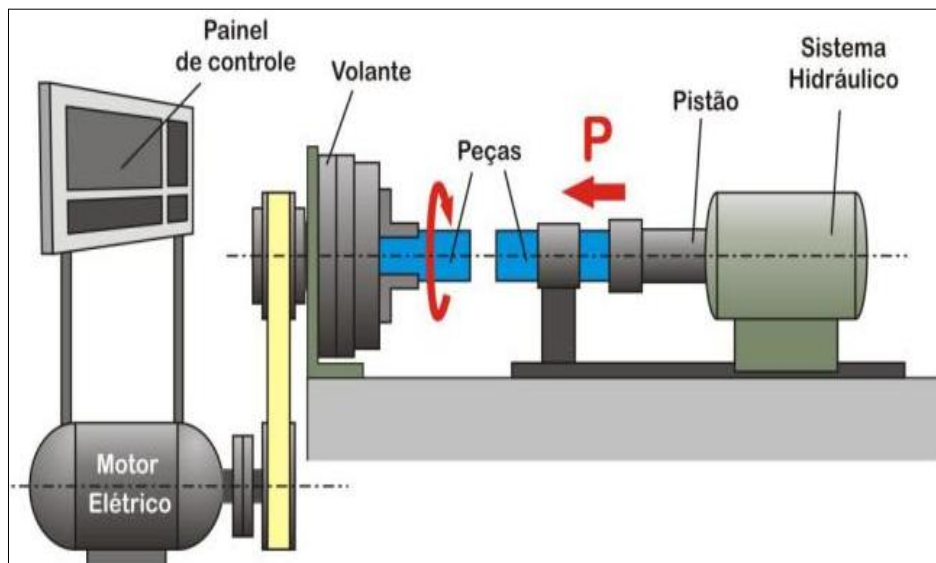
Equipamento de soldagem por fricção inercial.
